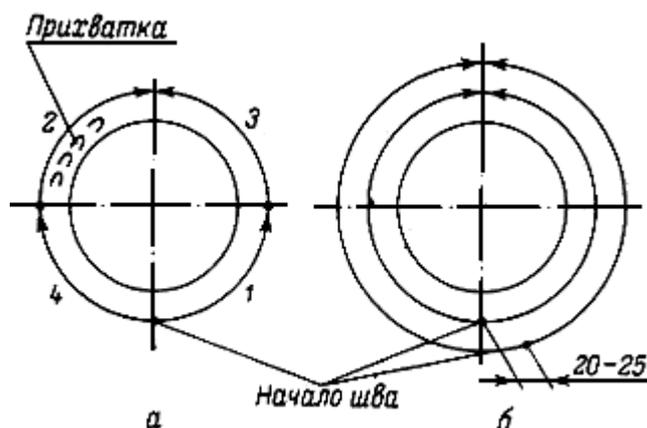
Последовательность сварки неповоротного стыка:
